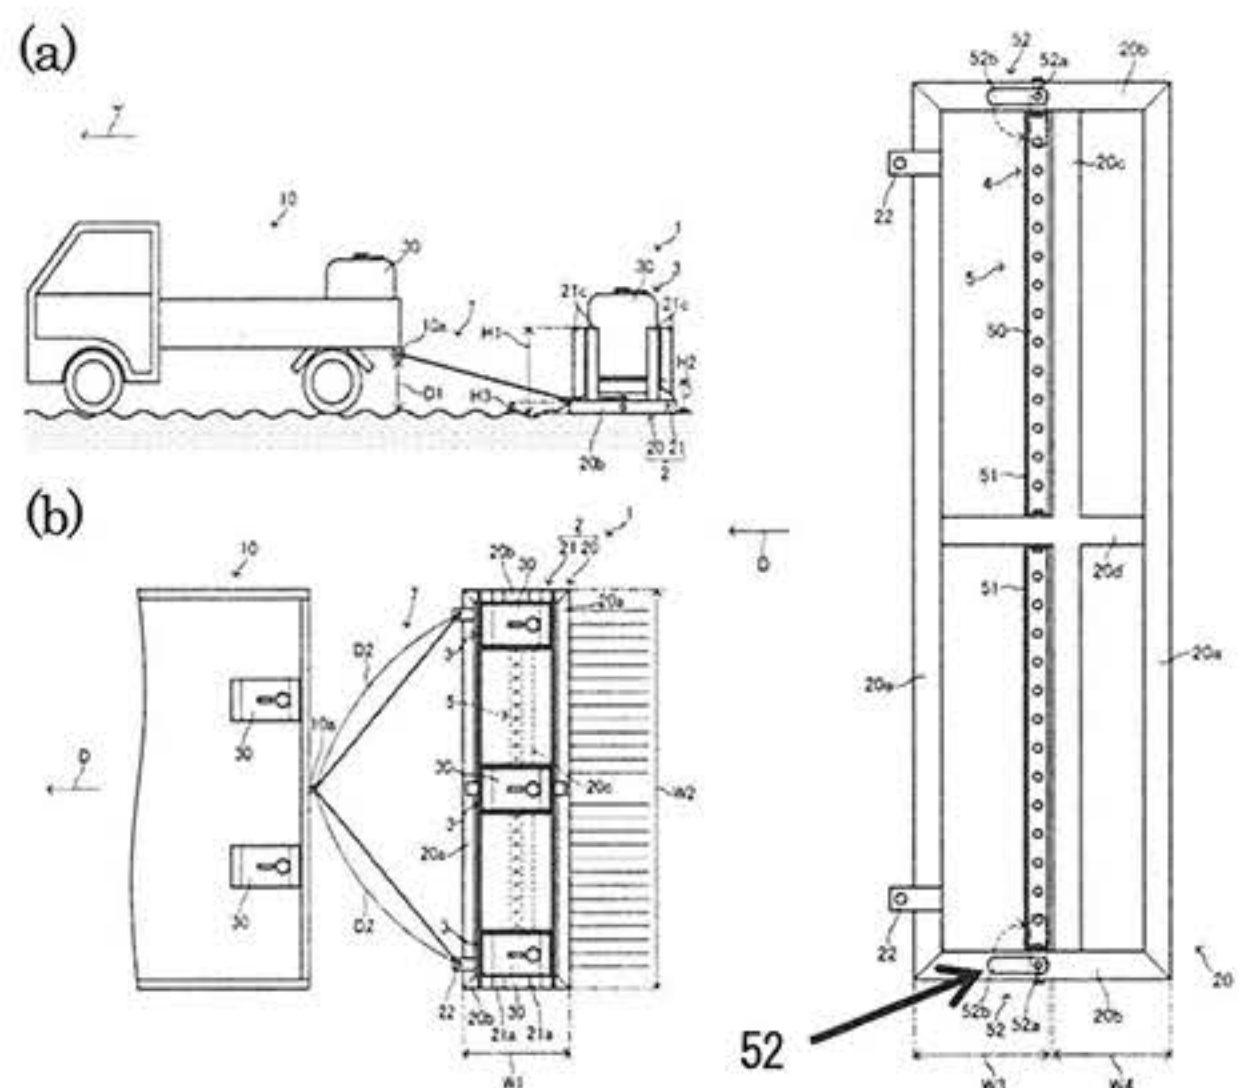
(a) 車両牽引(断面図) (b) 車両牽引(平面図)
